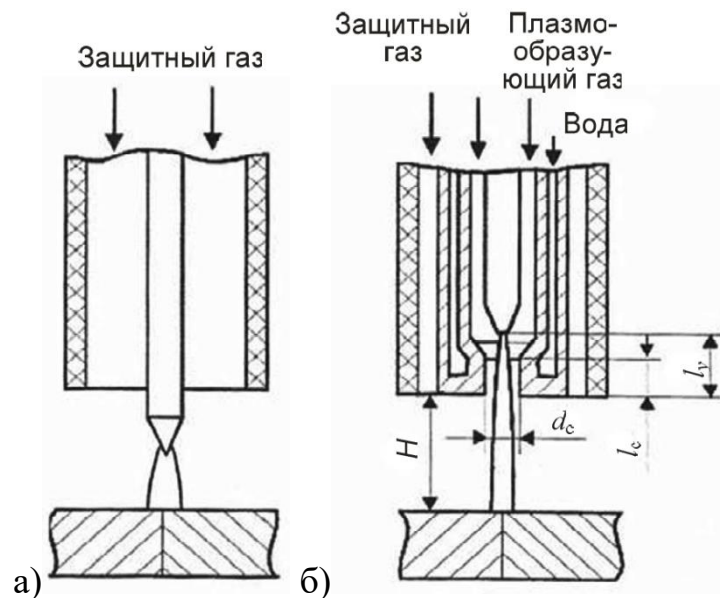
Схеми процесів TIG (а) і плазмового (б) зварювання [12].
